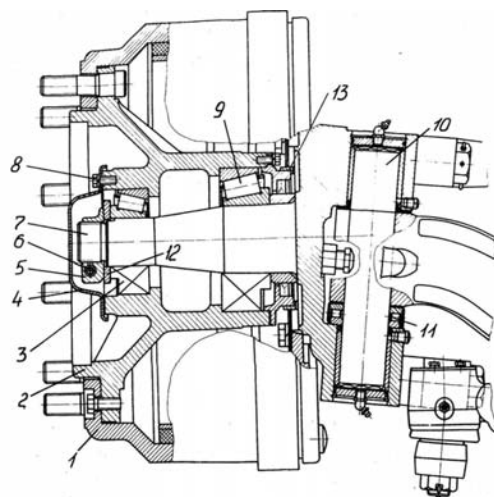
Передняя ось и ступица переднего колеса при установке дисковых колес: 1 — тормозной барабан; 2 — ступица; 3, 9, 11 — подшипники; 4 — крышка; 5 — гайка; 6, 8 — болты; 7 — кулак поворотный; 10 — шкворень; 12 — шайба; 13 — индуктор АБС; 14 — подшипник
